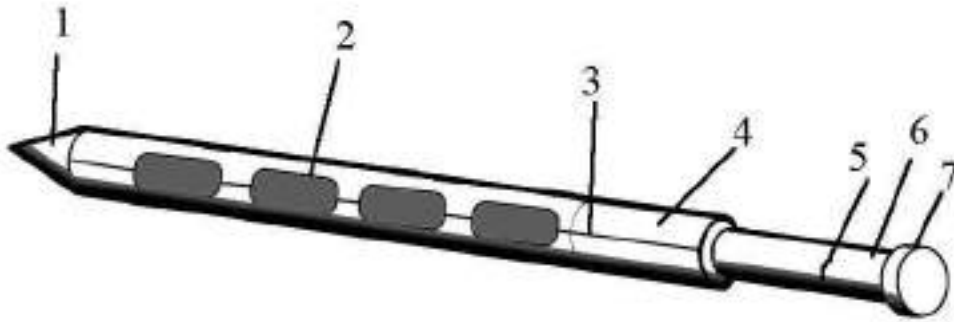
Щуп для бутылей: 1 - конус; 2 - окно; 3 - риска; 4 - наружный цилиндр; 5 - деление; 6 - внутренний цилиндр; 7 – ручка
